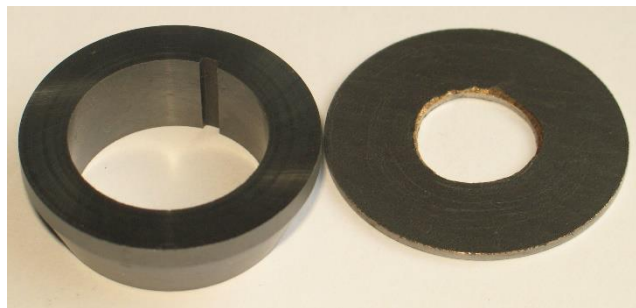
образцы для испытаний 1 – кольцо из ВК8, 2 – кольцо с РЕЕК
